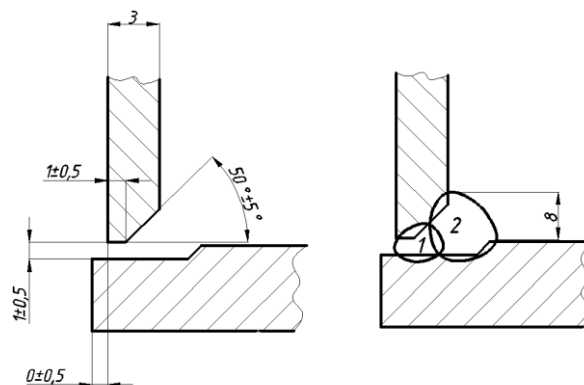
Тип сварного соединения У19 по ГОСТ 16037-80
